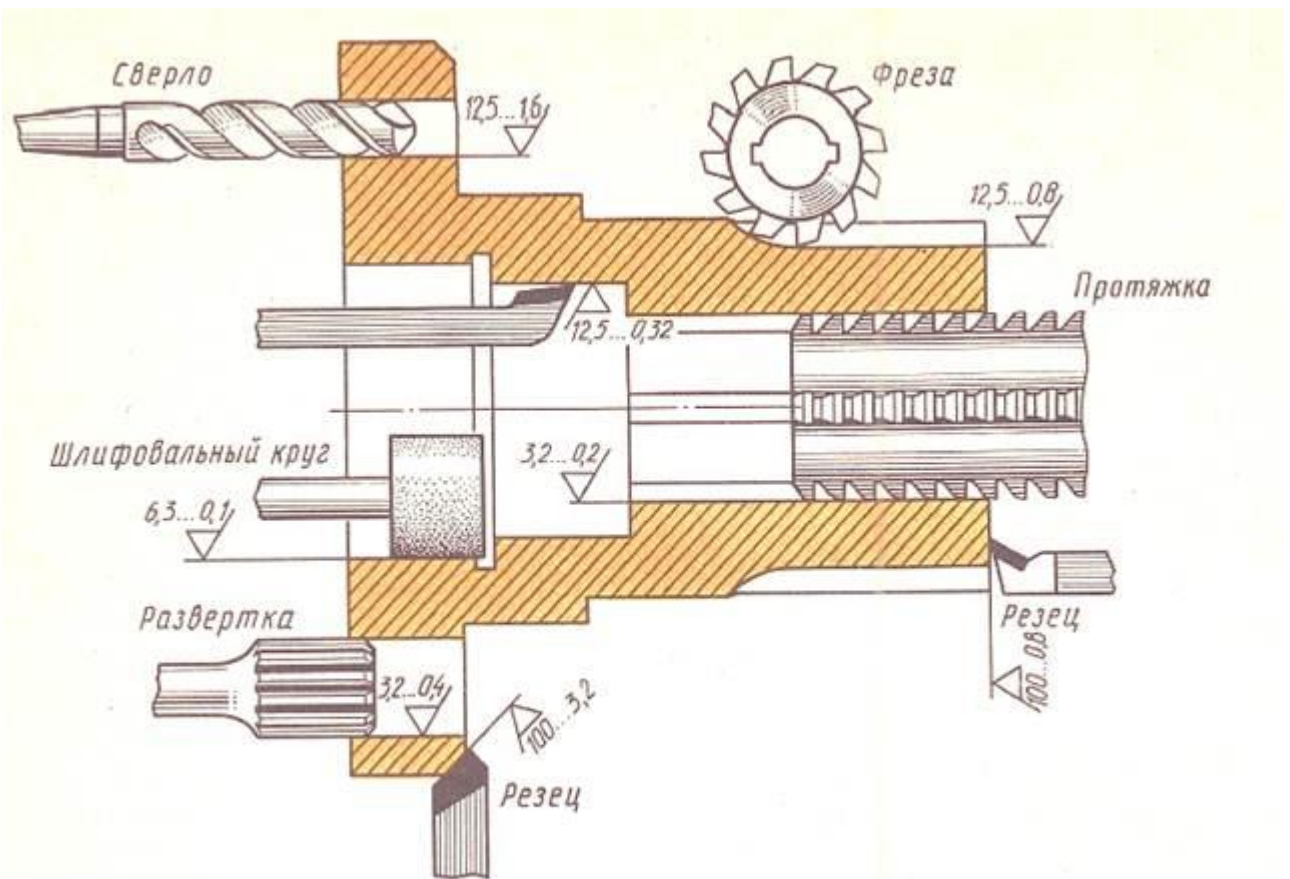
Примерная шероховатость поверхностей, получаемая при обработке различными способами
